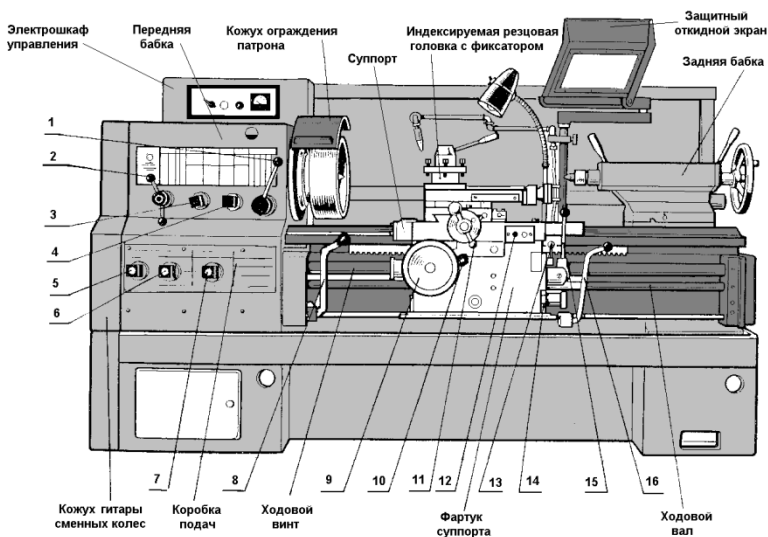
Общий вид токарно-винторезного станка 1B62Г
